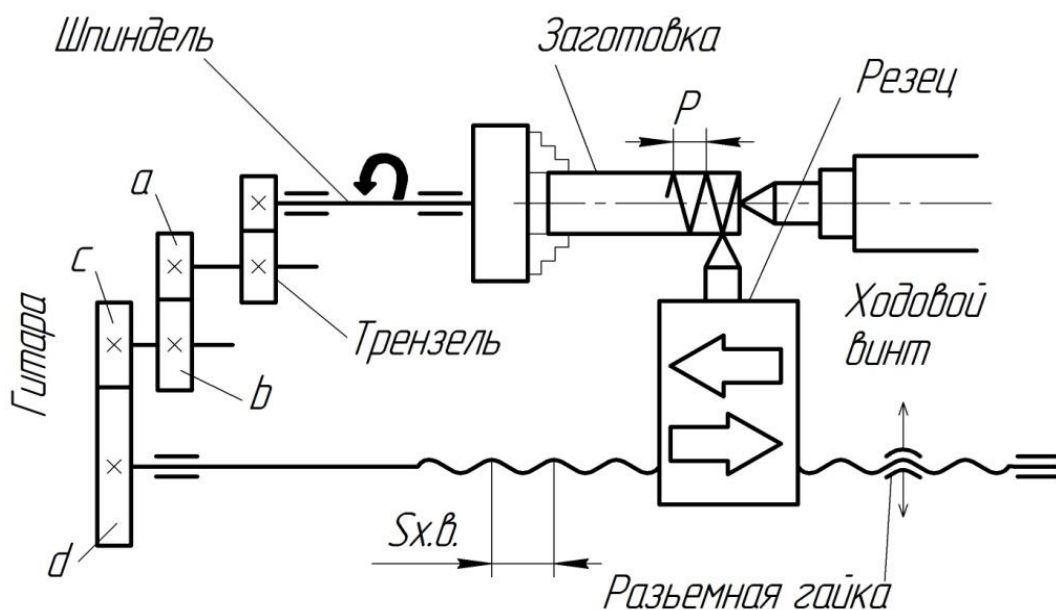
Схема настройки токарно-винторезного станка на нарезание резьбы
